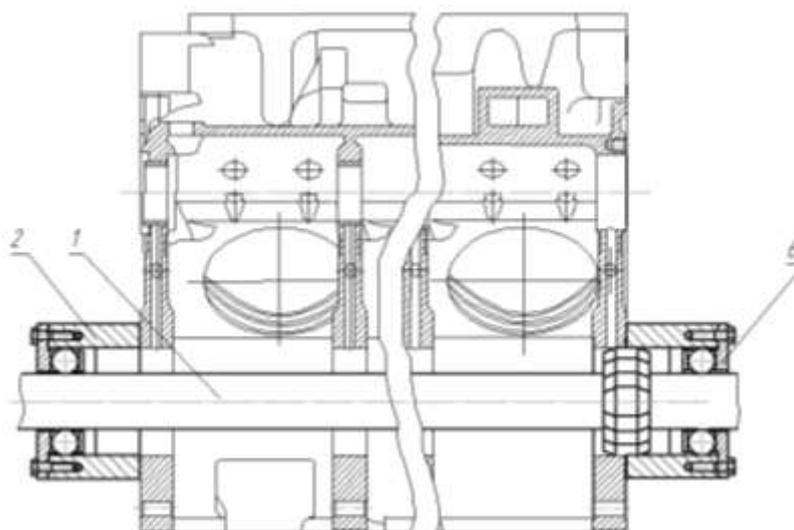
Обработка отверстий коренных опор под вкладыш коленчатого вала
